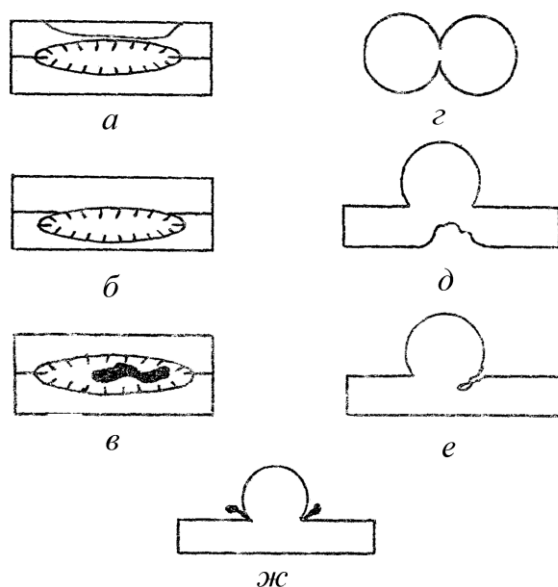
Точечные микросварные соединения с различными видами брака: а, б, в – при сварке деталей типа лист+лист; г – провод+провод; д, е, ж – провод+лист
